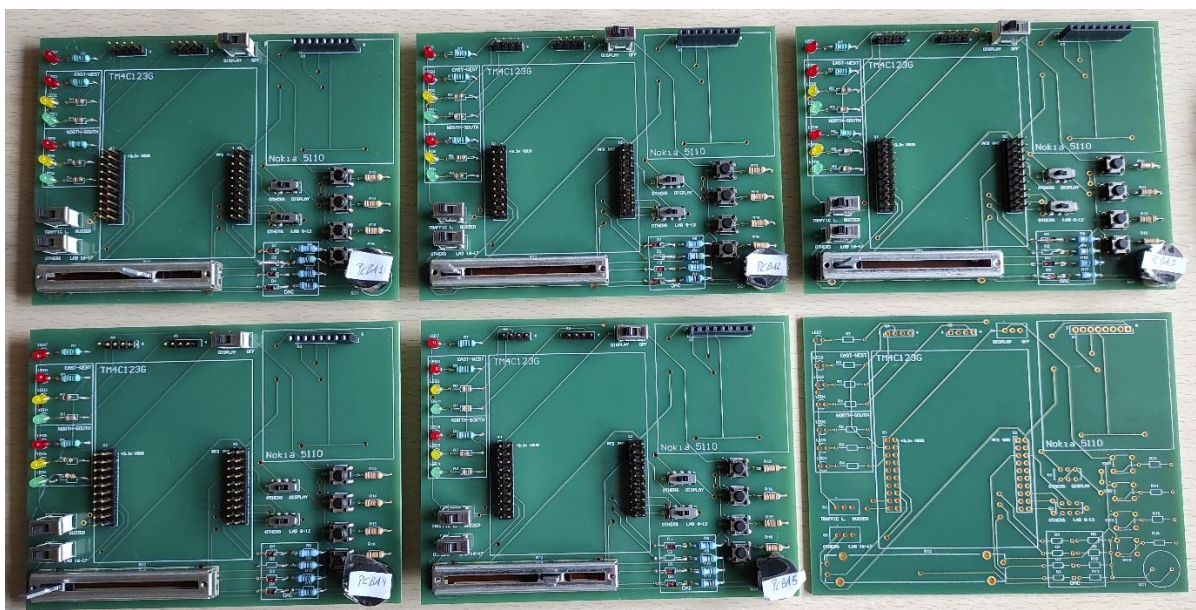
Vista frontal de les 5 PCBAs i la PCB sobrant.
